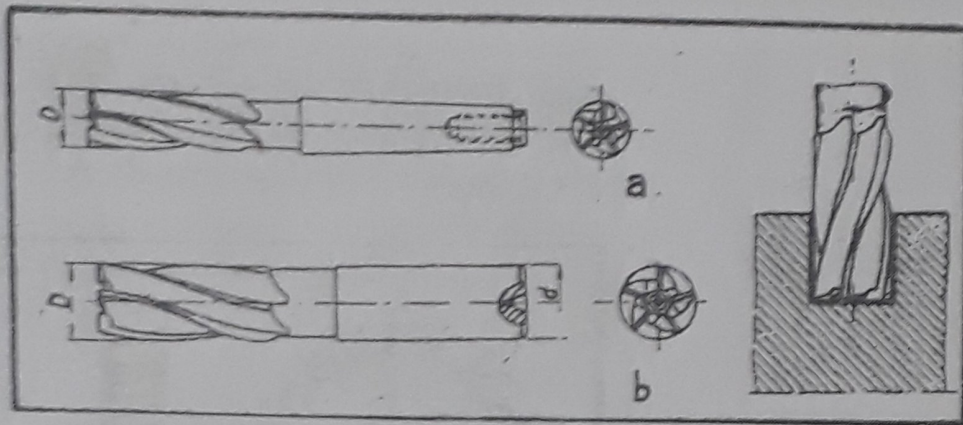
/3. — Fresa frontal integral: a) Vástago cónico; b) Vástago cilíndrico.
